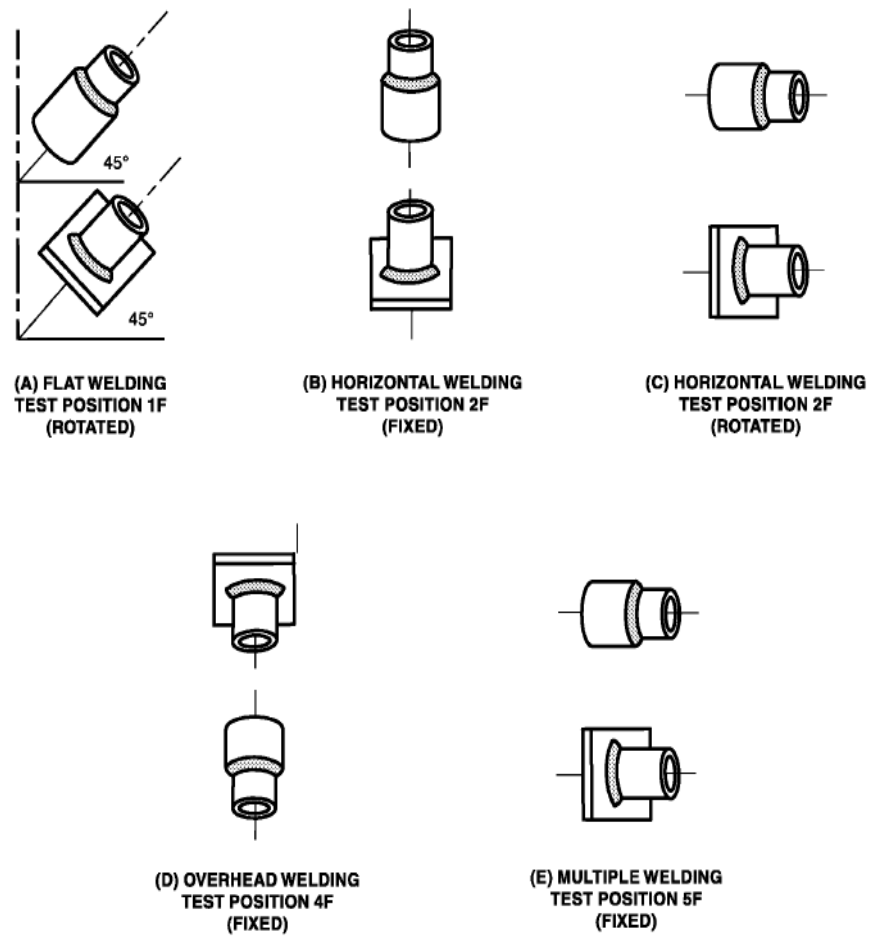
Posición de Muestras de Tuberías para Soldaduras Filete (9).
